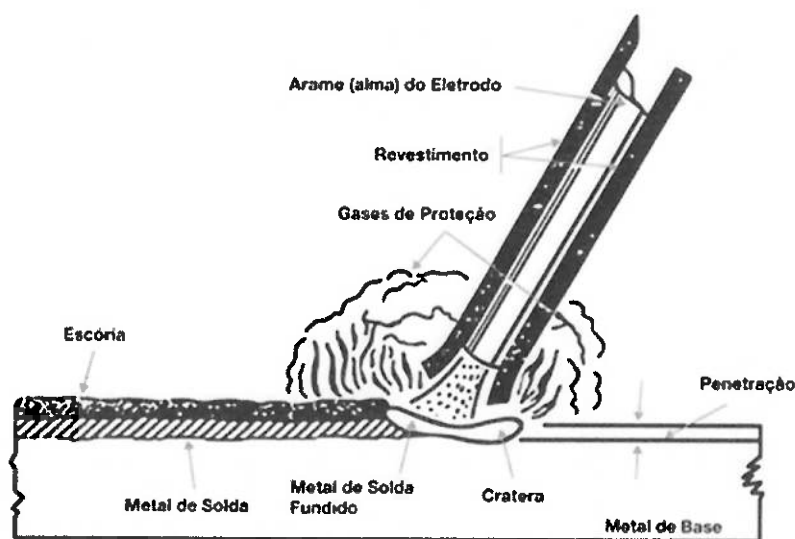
Processo de soldagem SMAW (ESAB, 2015)
